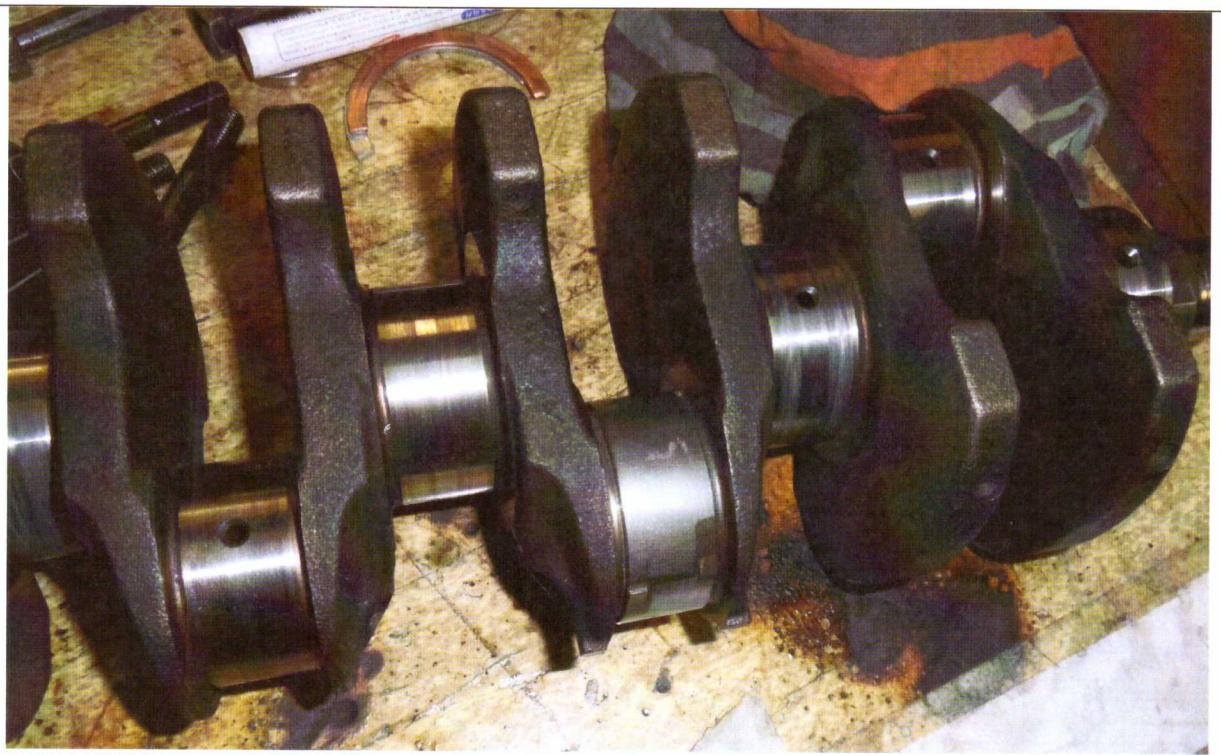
Общий вид шеек коленчатого вала двигателя после аварийного цикла испытаний. Базовый двигатель.
